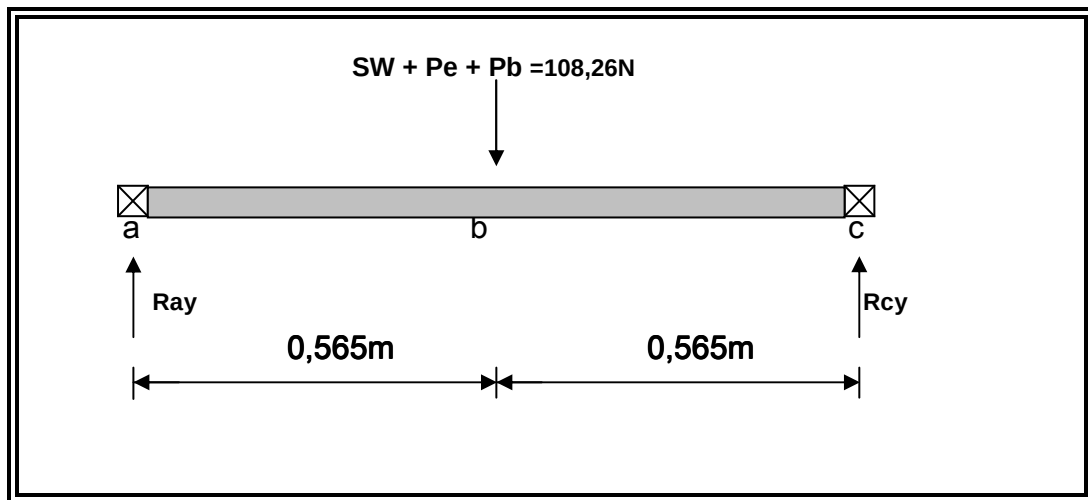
fuerzas aplicadas sobre el eje en el plano “YZ” del transportador N° 1. Fuente:
